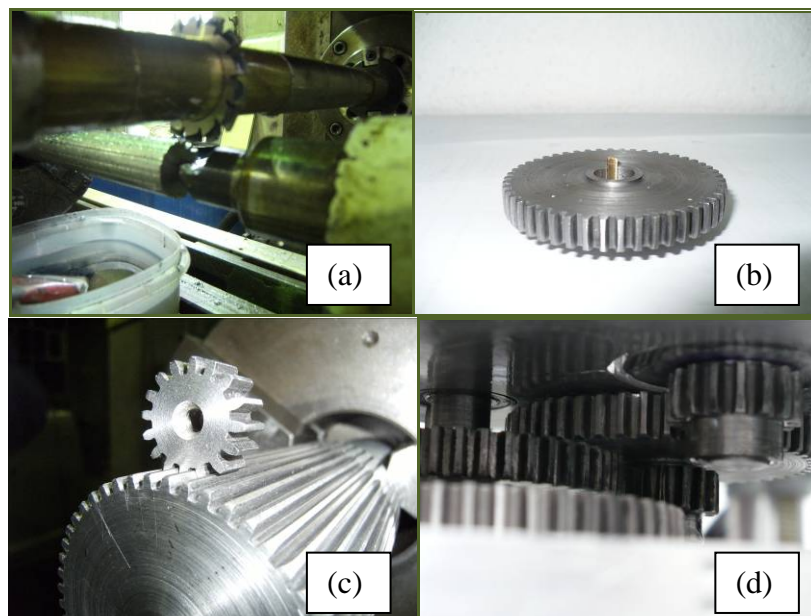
(a) Construcción de los engranes, (b) Engrane, (c) Verificación del engranaje, (d) Transmisión armada.
